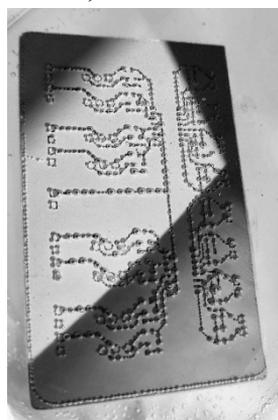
Процесс вытравливания заготовки (раствор зелёного цвета)
